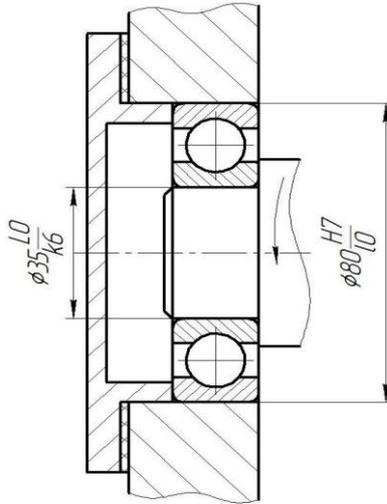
Обозначение посадок подшипника на вал и в корпус
